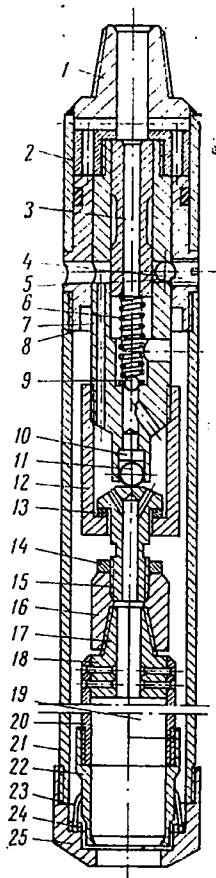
Двойной колонковый снаряд ДКС-2-ТПИ.
